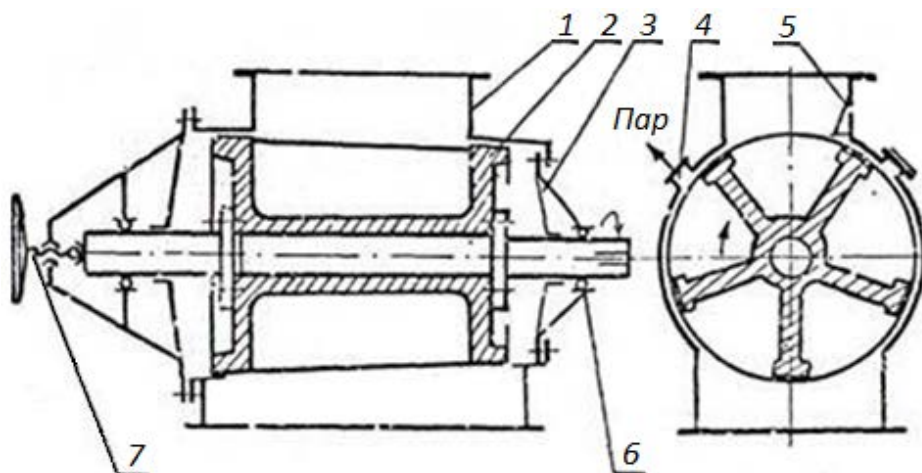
Питатель низкого давления: 1 – корпус; 2 – ротор; 3 – крышка; 4 – патрубок для отвода пара из карманов ротора; 5 – шабер; 6 – подшипник; 7 – механизм присадки ротора
